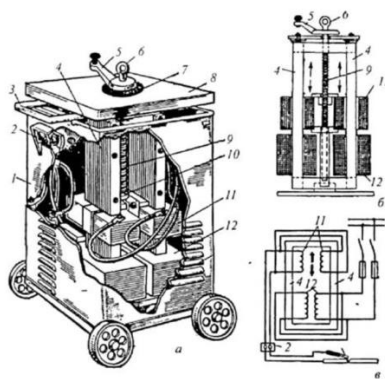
Сварочный трансформатор: а – внешний вид; б – схема регулирования сварочного тока; в – электрическая схема; 1 – корпус; 2 – зажим; 3 – ручка; 4 – магнитопровод; 5 – рукоятка; 6 – рымболт; 7 – шкала; 8 – крышка корпуса; 9 – вертикальный винт; 10 – ходовая гайка винта; 11, 12 – вторичная и первичная обмотки соответственно
